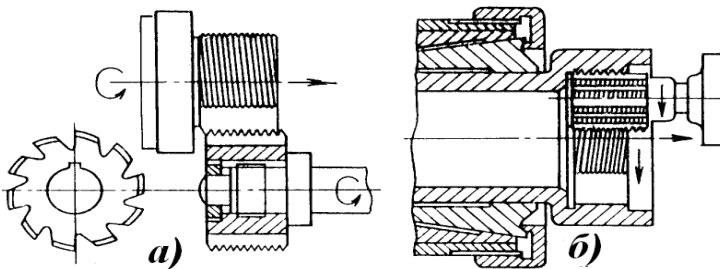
Схема нарізання різьби гребінчастою фрезою:
